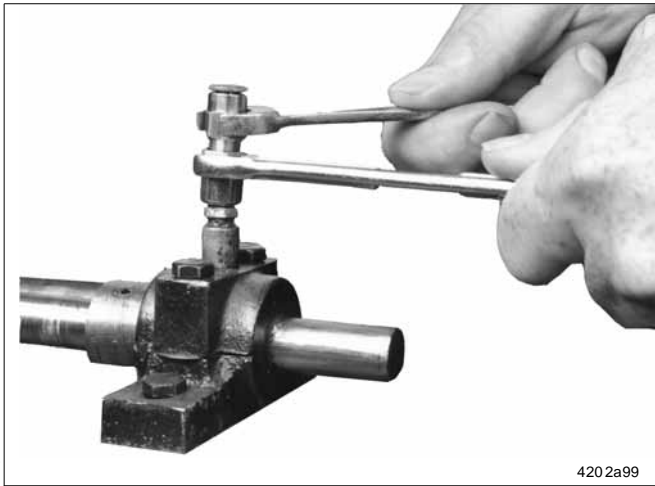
Quicklinc-Steckverschraubung in den Zerk-Lock-Körper einschrauben
